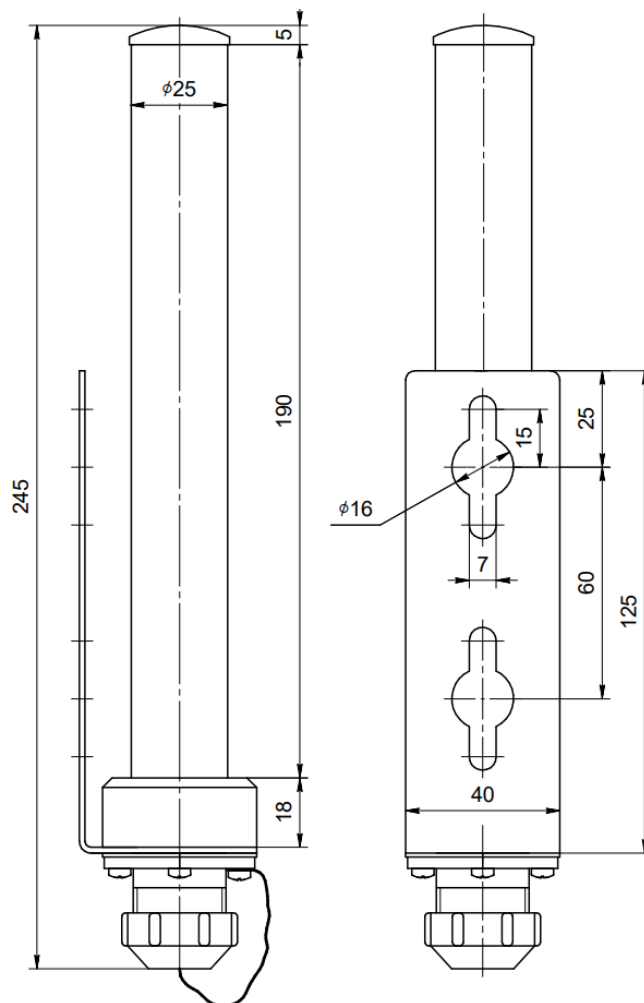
Габаритные и присоединительные размеры ПС-150(РК)
